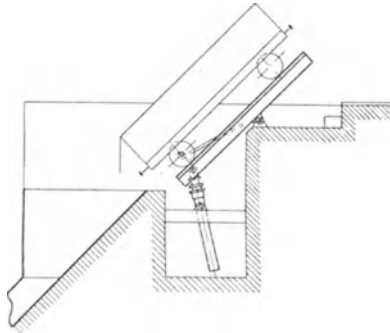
Selbsttätiger Stirnkipper mit hydraulischem Kolben.
